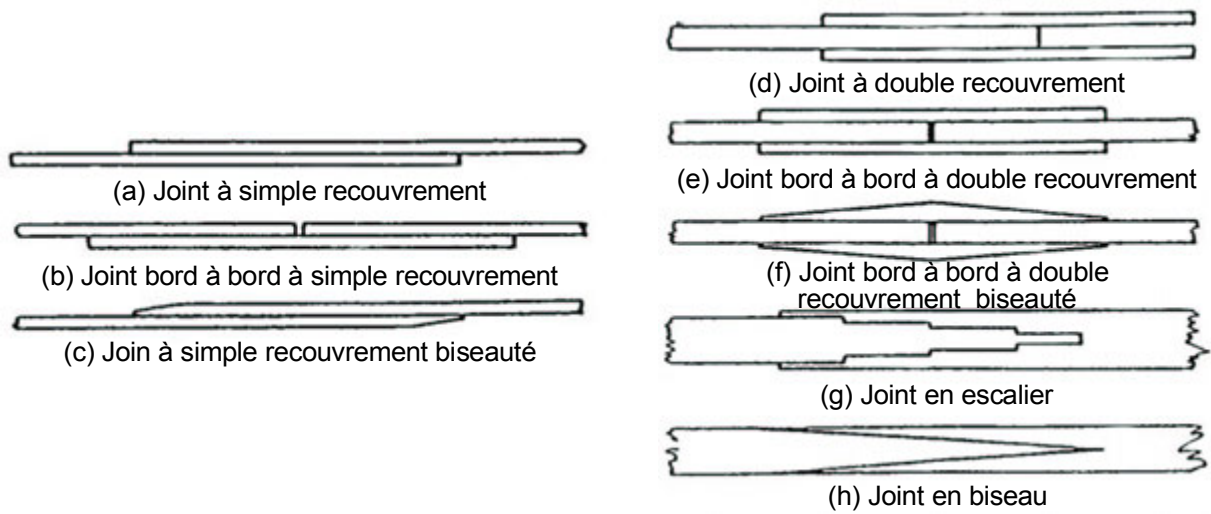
Joints collés : de (a) à (c), joints à simple recouvrement, et de (d) à (h), joints à double recouvrement et leurs variantes
